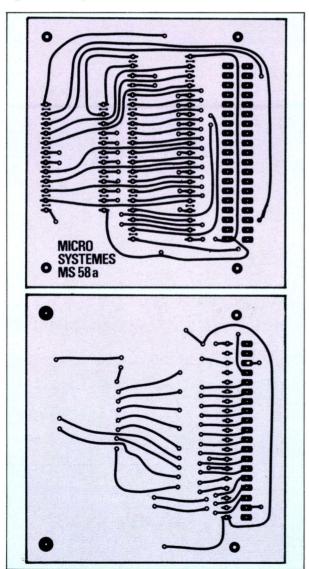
Circuit imprimé de la carte de base vue côté soudures et côté composants.
